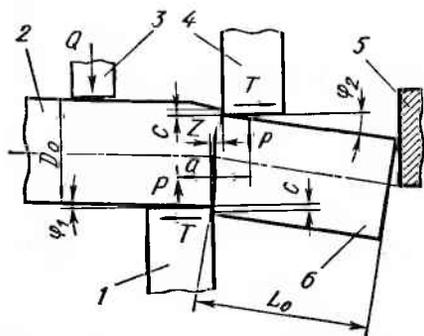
Схема резки прутка сдвигом: 1 — нижний (неподвижный) нож, 2 — пруток, 3 — прижим, 4 — верхний (подвижный) нож, 5 — упор, 6 — отрезанная заготовка
